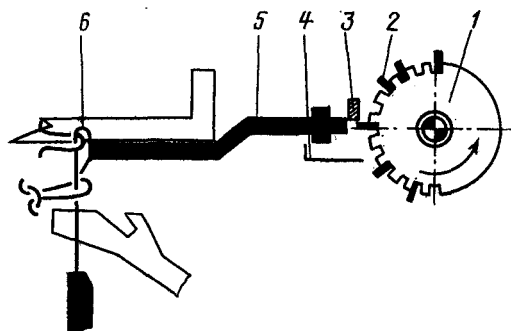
Схема отбирающего барабана для управления индивидуальными прессами
